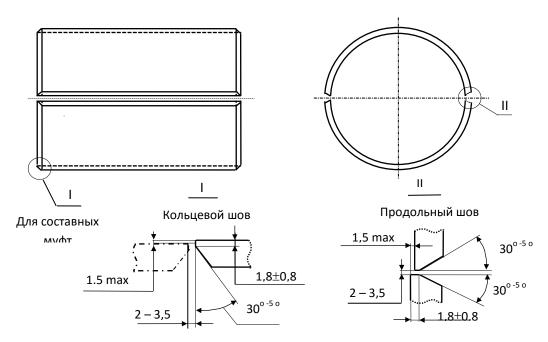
Разделка кромок полумуфт под сварку
